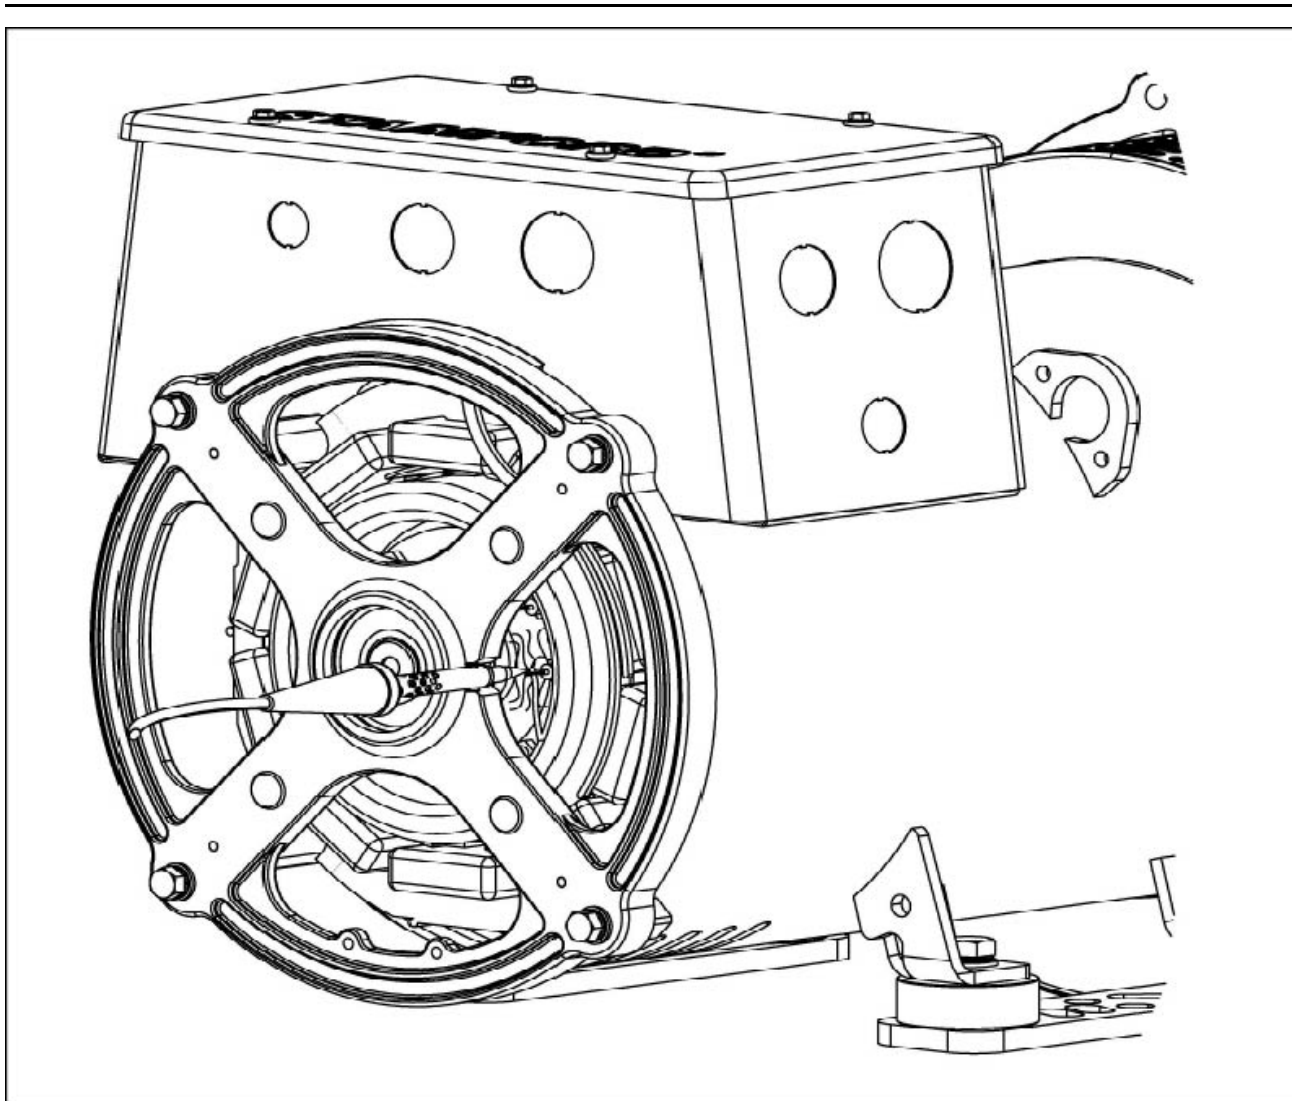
DÉPOSE DE LA SOUDURE DE LA DIODE
